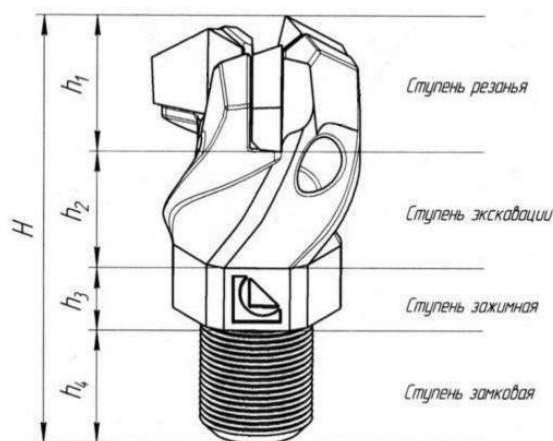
Резец РПА-27-3/14 после модернизации
